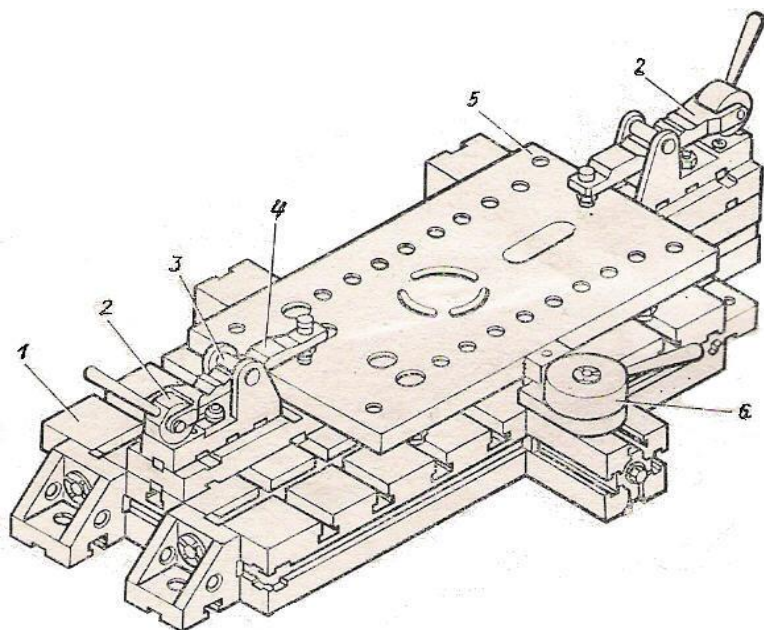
Универсально-сборный штамп, собранный с применением базовых элементов УСП-12
